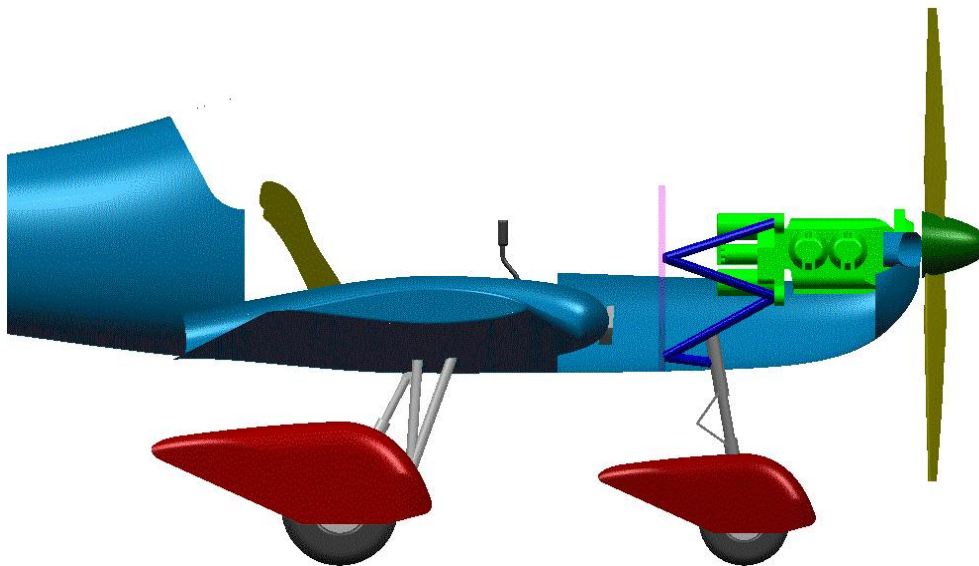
Dimensões da Cabine e Instalação do Motor – Vista Lateral
